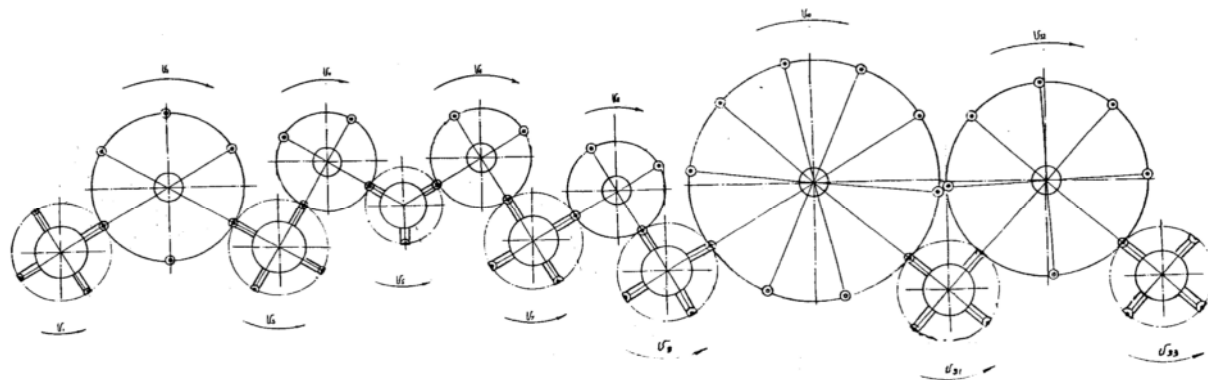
Компоновочная схема автоматической роторной линии для изготовления детали “Втулка” КГУЗ.024.ПРУ.
